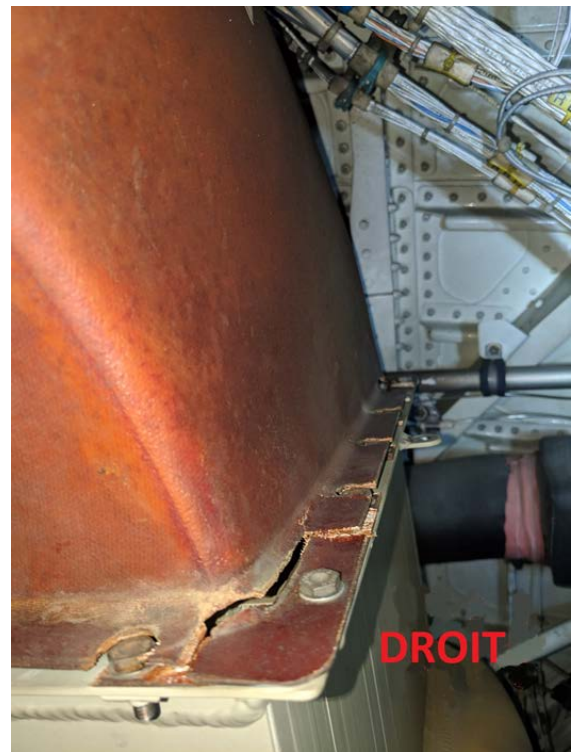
Bord du conduit gauche arrière séparé Fig 3 : Conduit droit extérieur
